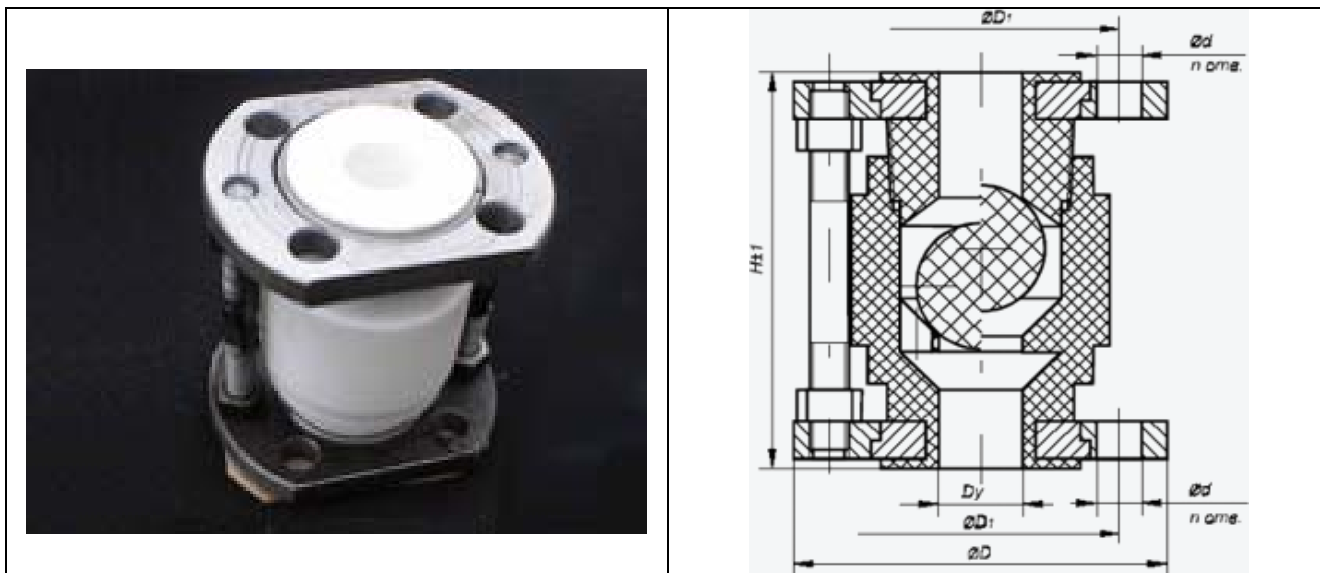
Обратный шаровой клапан с проточной частью из фторопласта-4 (КОШФ)
